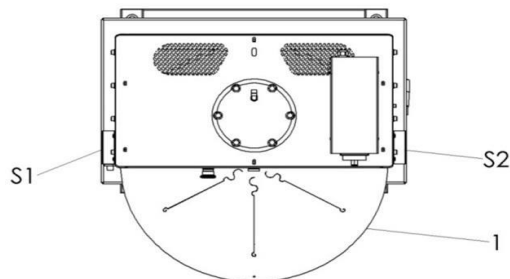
Máquina de prato rotativo (dublar) - vista frontal
